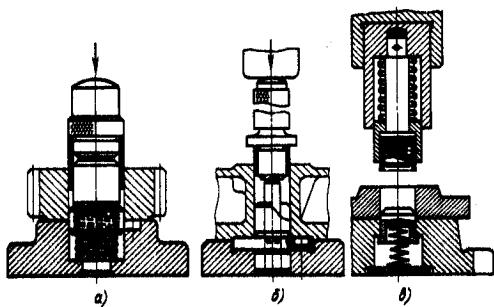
Приспособление для запрессовки втулок: а — пружинное; б — с направляющим стержнем; в — с закреплением втулки на ползуне
